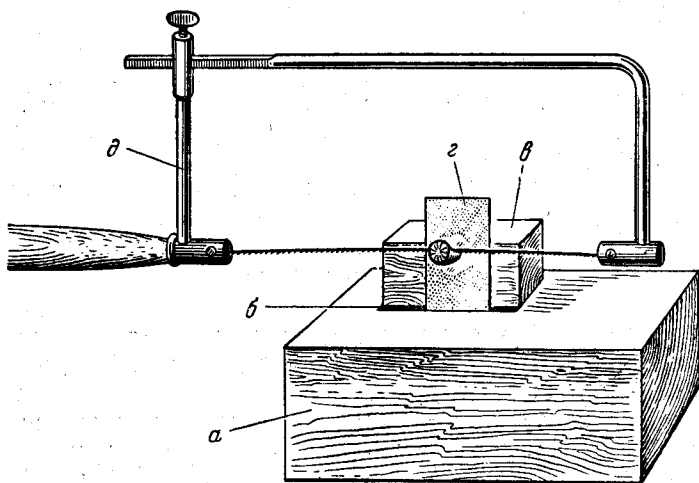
Деревянный брусок — подставка для шлифа при ручной пилке
